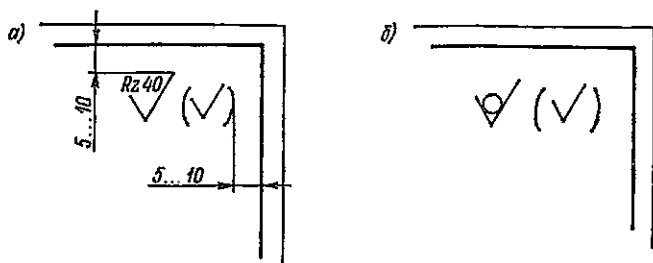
Простановка знаков преобладающей шероховатости или шероховатости поверхностей, не обрабатываемых по данному чертежу
